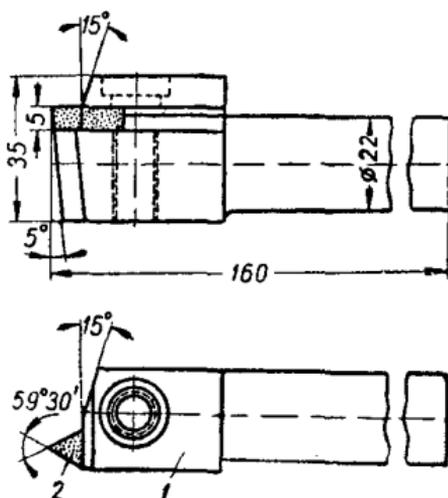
Резьбовой резец с механическим креплением пластинки из твердого сплава конструкции Д. И. Рыжкова.
